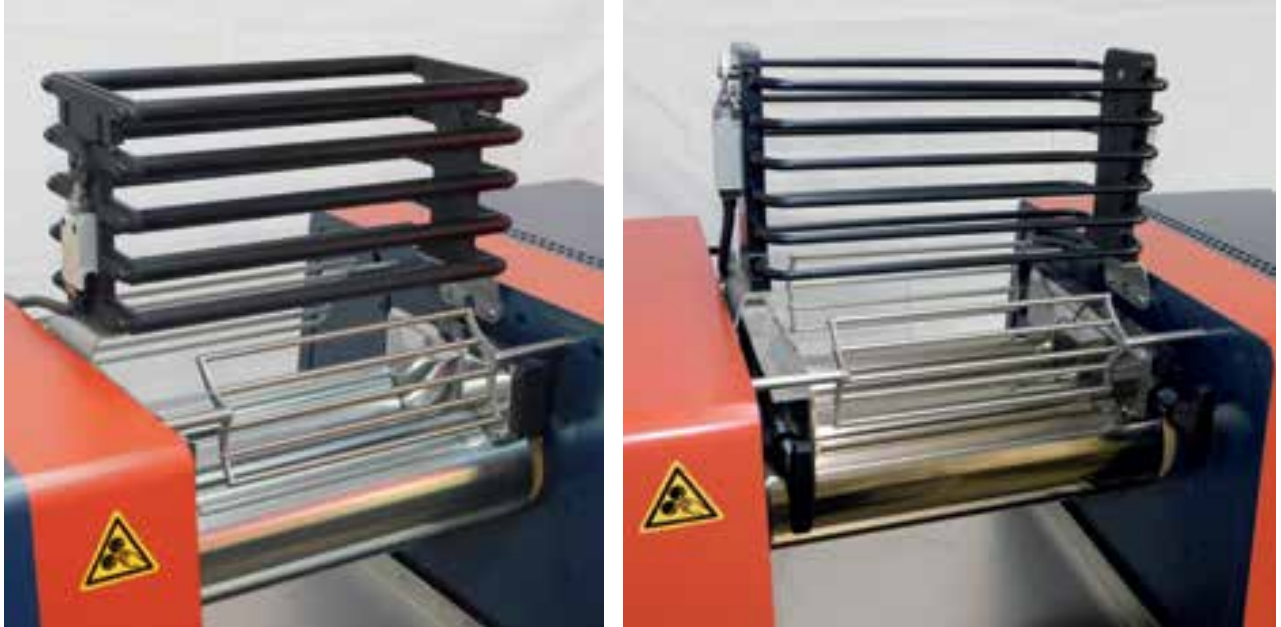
Schutzeinrichtungen an einem Laborwalzwerk
